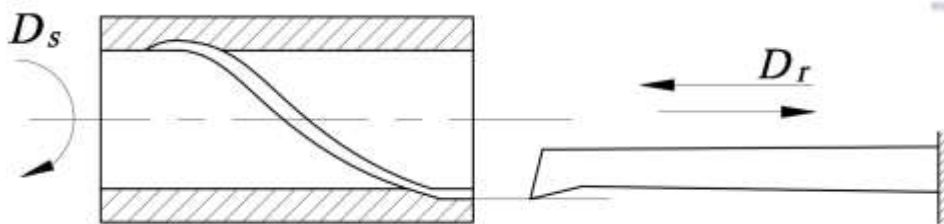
Схема формування гвинтових пазів втулок довбальними різцями
